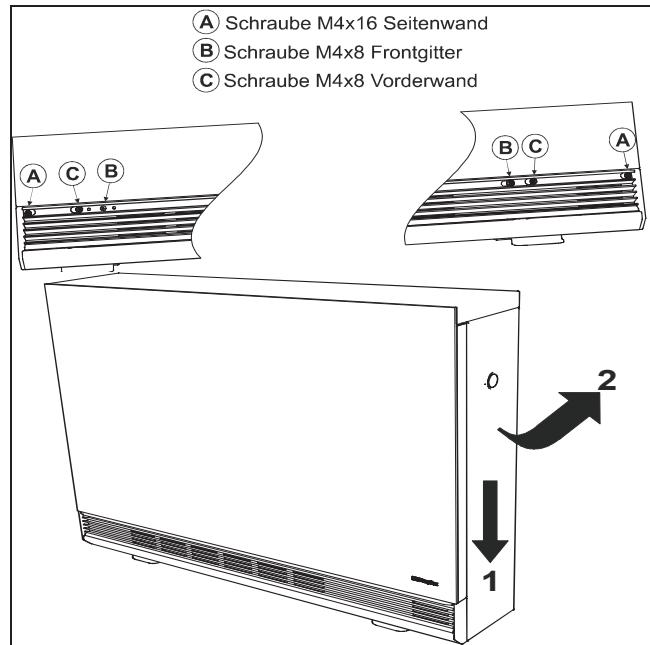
Schrauben der beiden Seitenwände entfernen (A). Die Seitenwände nach unten schieben (1) und ausschwenken (2). Nach Abnehmen der Seitenwände die Befestigungsschrauben (B) des Frontgitter lösen und das Frontgitter entfernen. Danach die Befestigungsschrauben (C) für die Vorderwand lösen.
